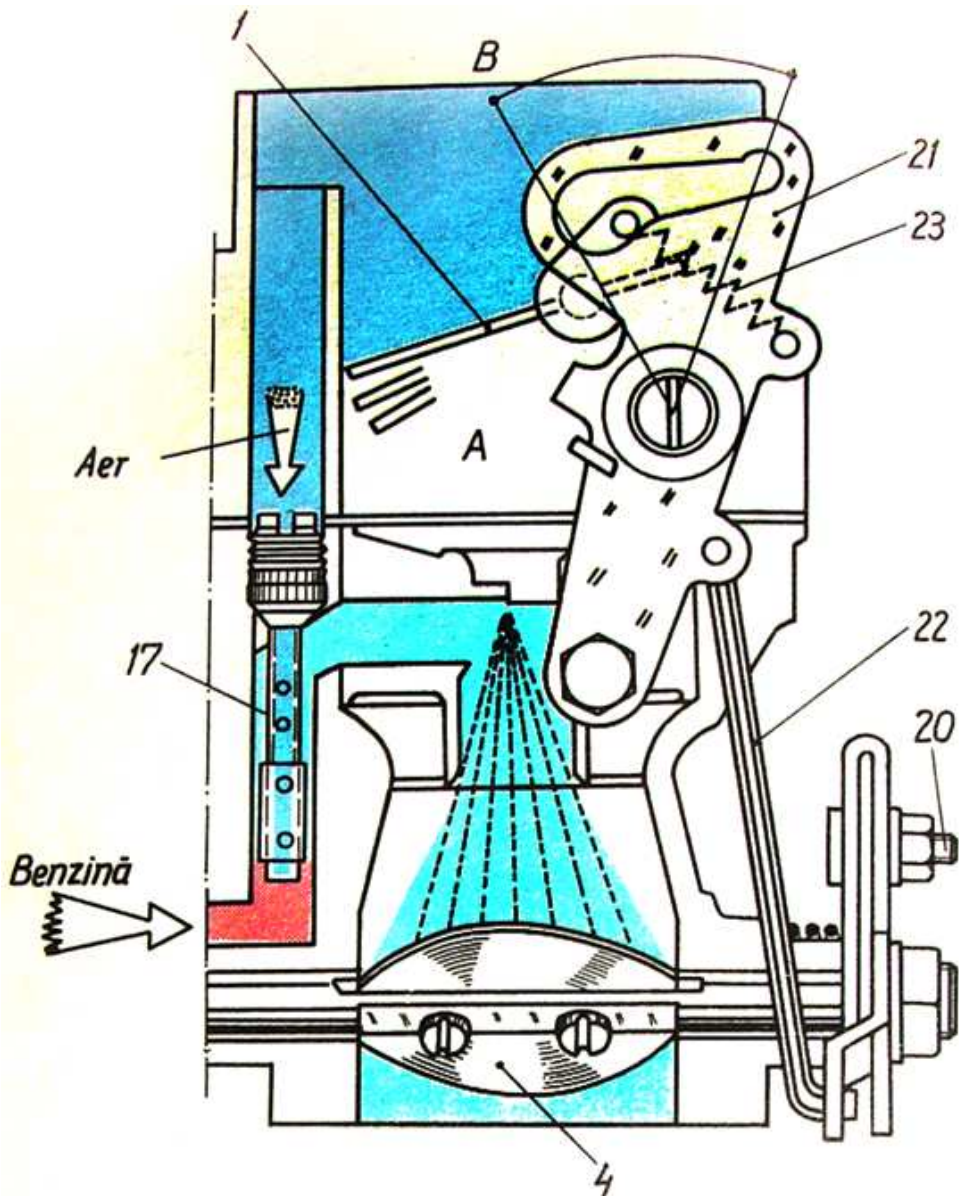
Carburator CARFIL-32-IRM-WEBER:
